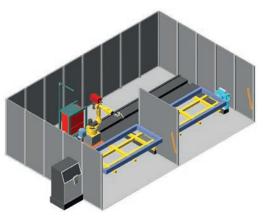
Схематичное изображение комплекса РК759 поворачивается в положение наиболее благоприятное для формирования сварного шва. Сварка швов выполняется на предварительно запрограммированных режимах сварки с контролем готовности сварочного источника и горения дуги.
